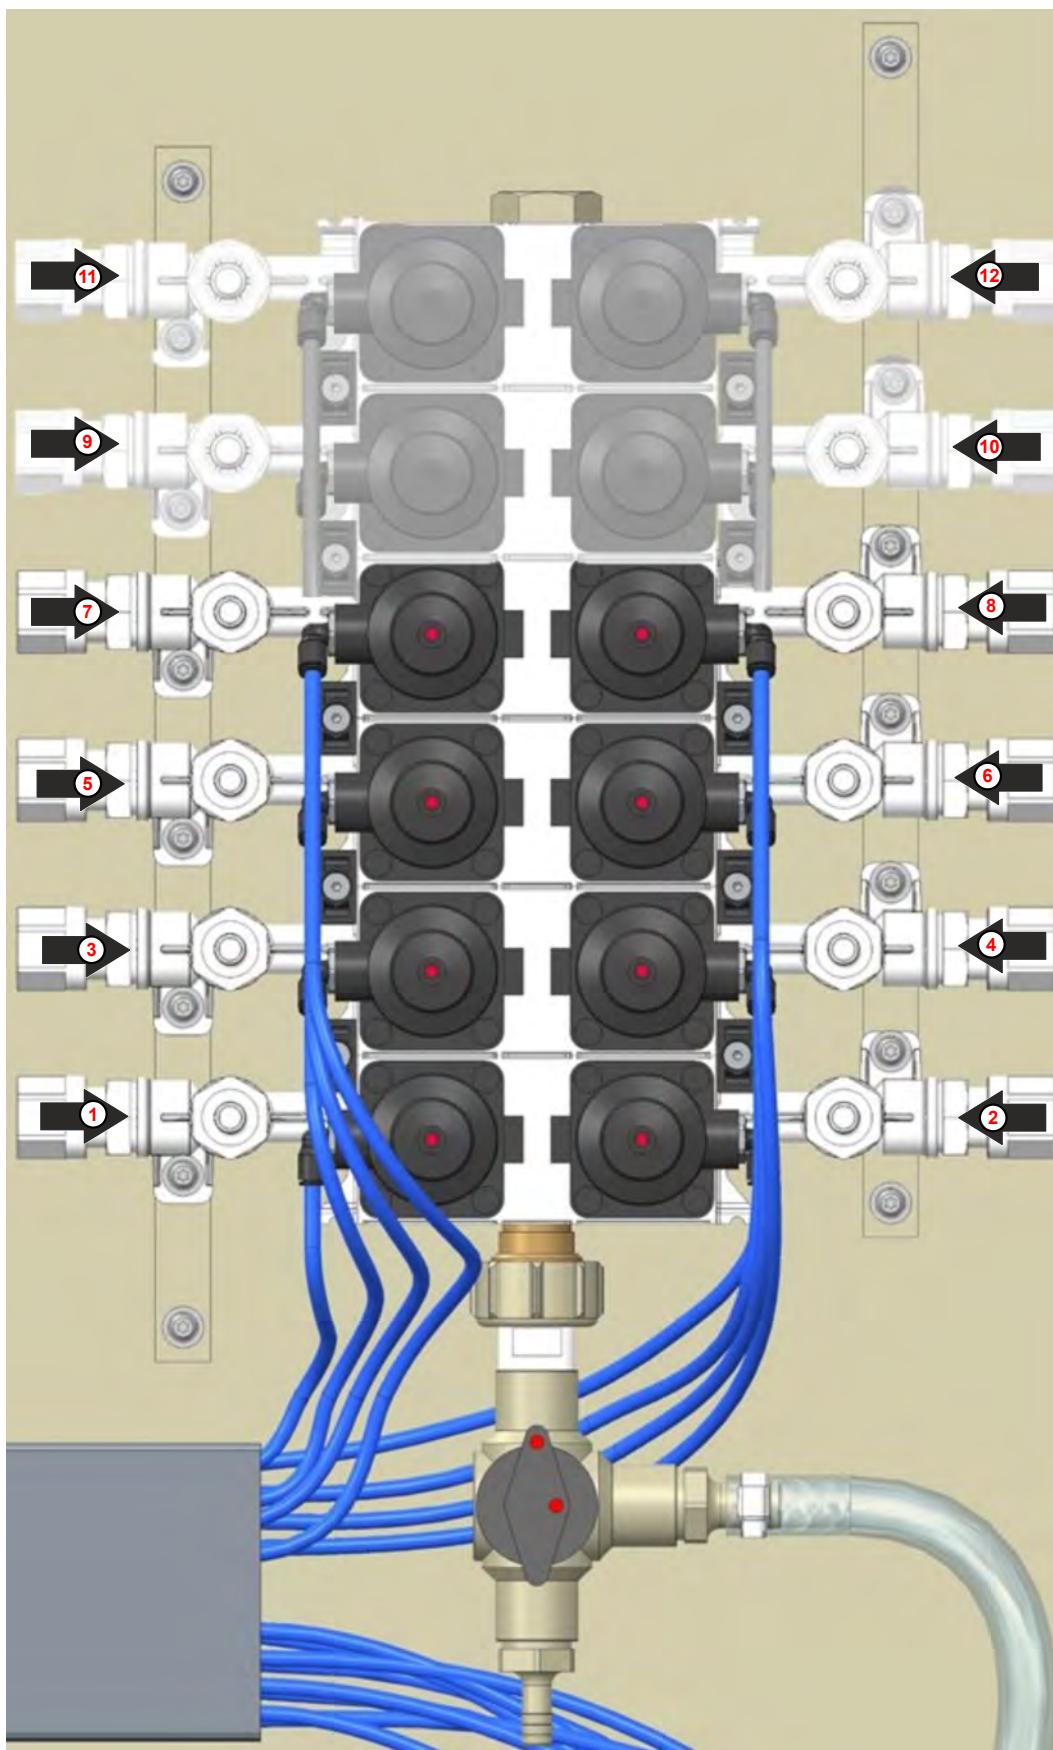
Membranventilverteilerblock / Maschinenzuordnung
